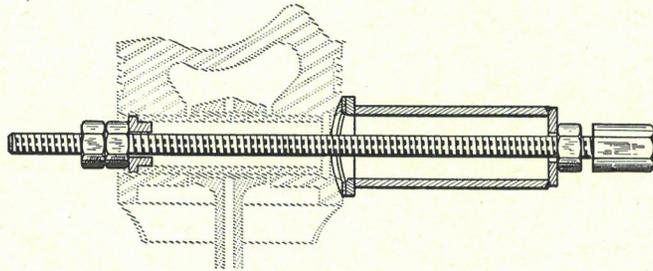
DÉMONTAGE DE LA BAGUE DE PIED DE BIELLE
